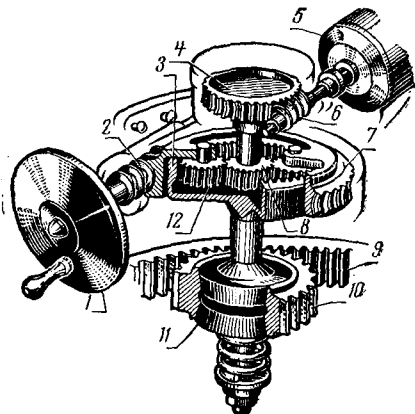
Механизм поворота башни с планетарной передачей в приводе:
